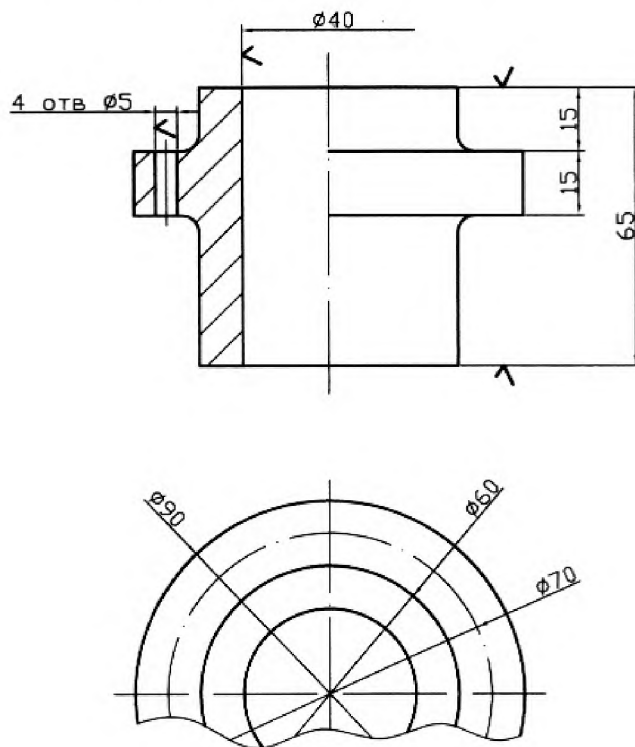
Эскиз детали «корпус» из чугуна СЧ 15
